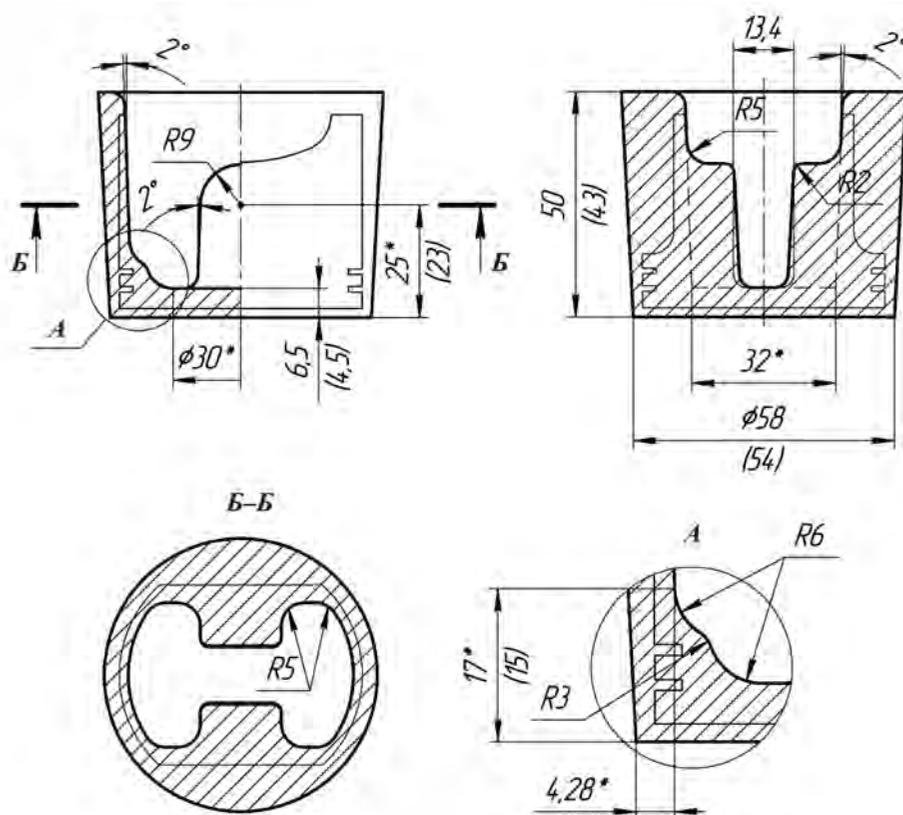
Чертеж штампованной поковки «поршень» из сплава АК4-1
